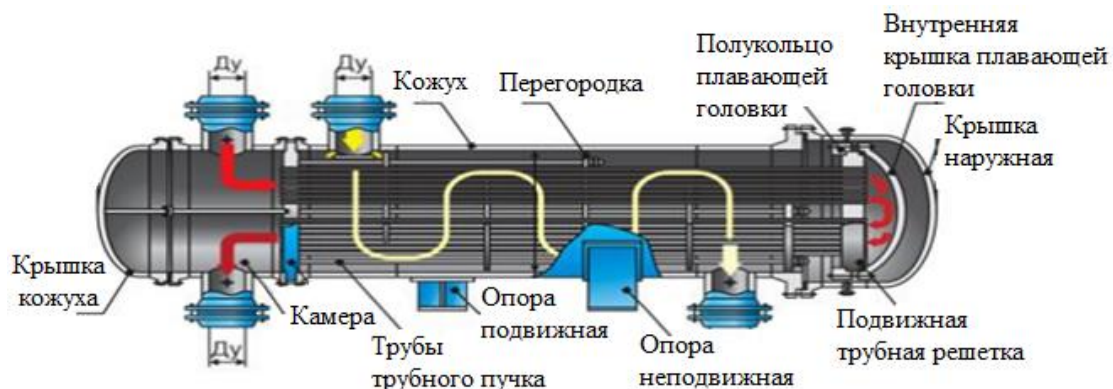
Кожухотрубчатый теплообменник с плавающей головкой [7, с. 47]
